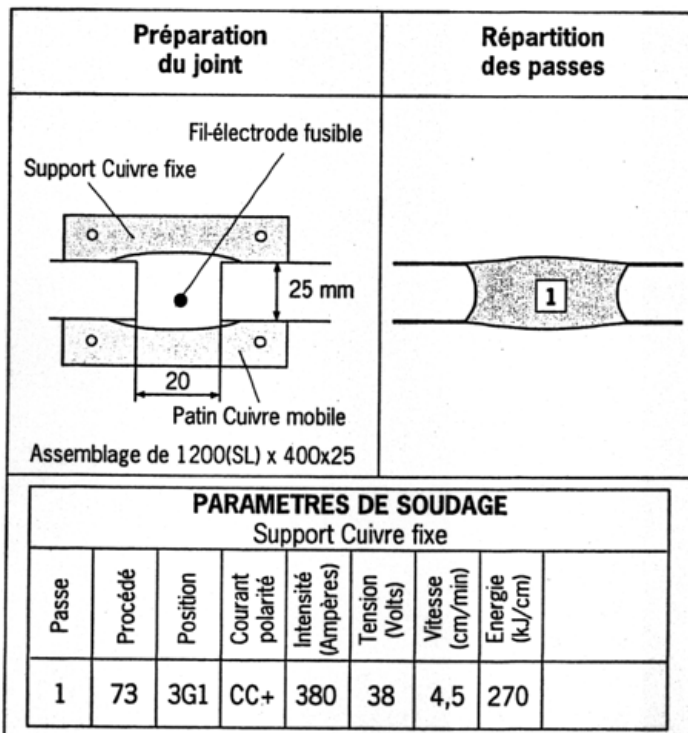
Procédé de soudage Vertishield (Lincoln)
